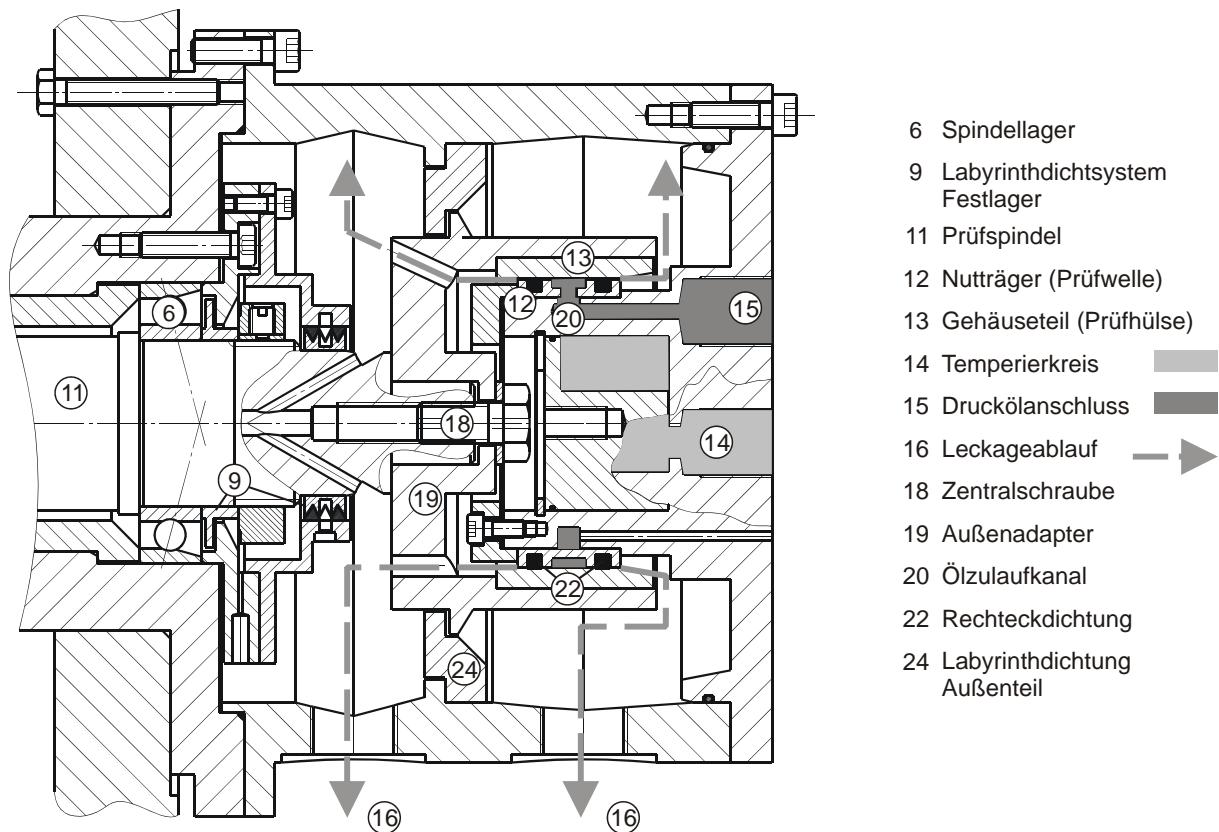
Detailansicht Prüfkopf mit rotierendem Außenteil
